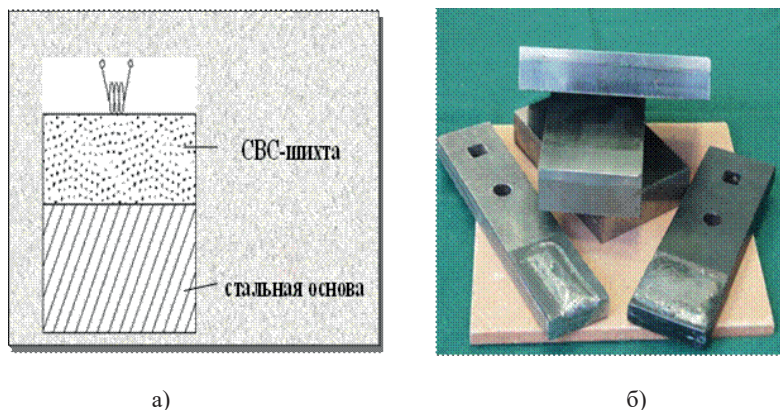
Схема наплавки (а) под давлением газа твердых сплавов на стальные основы (б)
